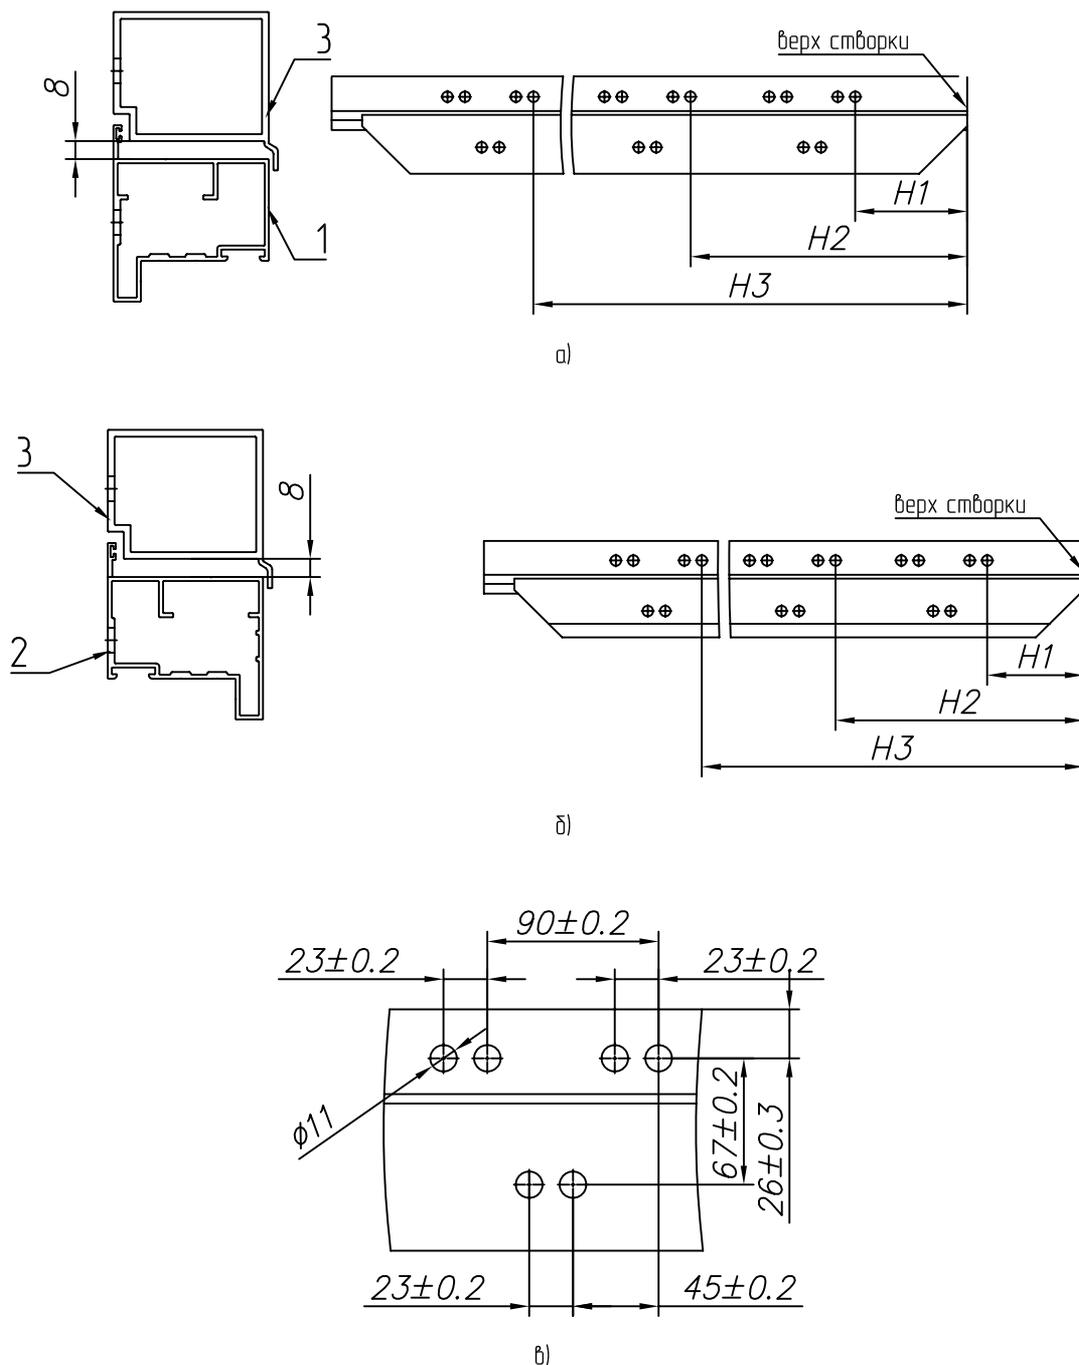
Изготовление групп отверстий для крепления петель:
